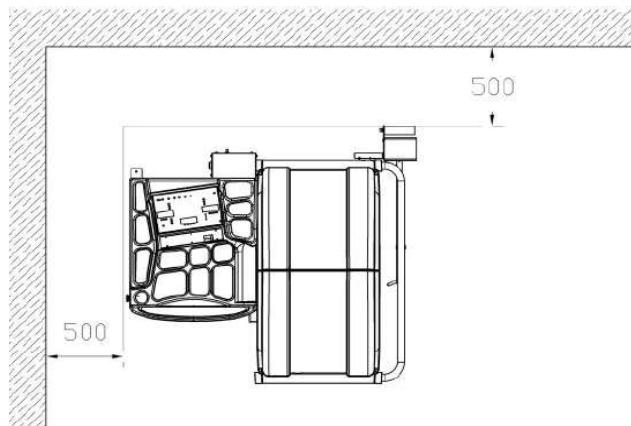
Local de instalação para máquina de balanceamento de rodas
